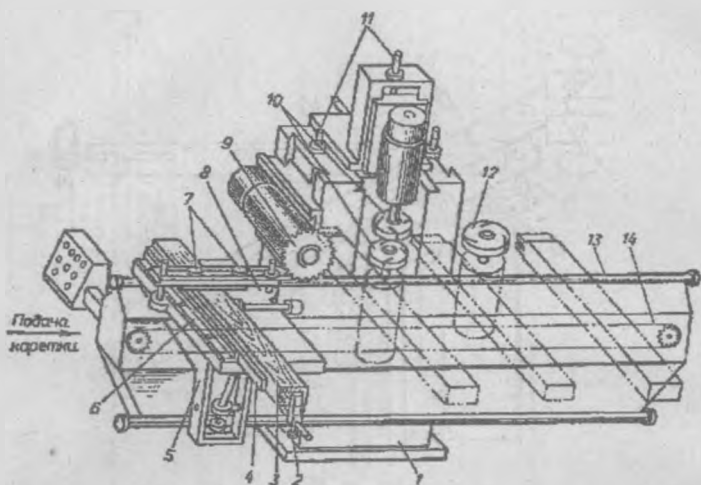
Односторонний шипорезный станок для рамных шипов:
